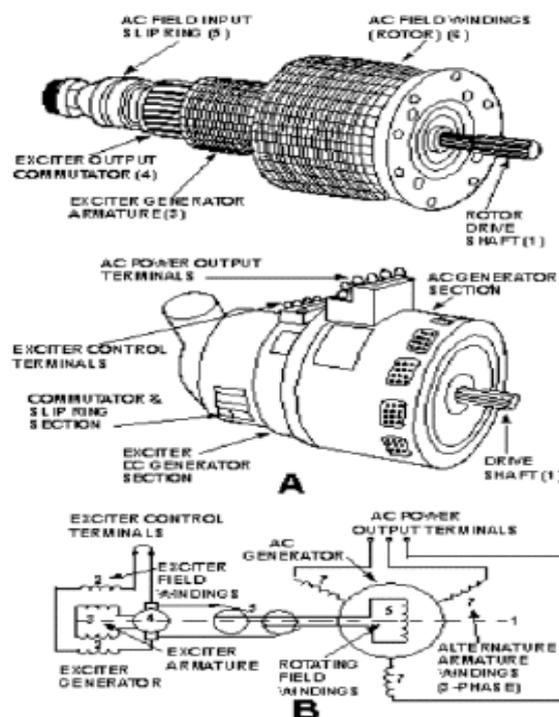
Rotor Kutub Silinder Generator Sinkron
